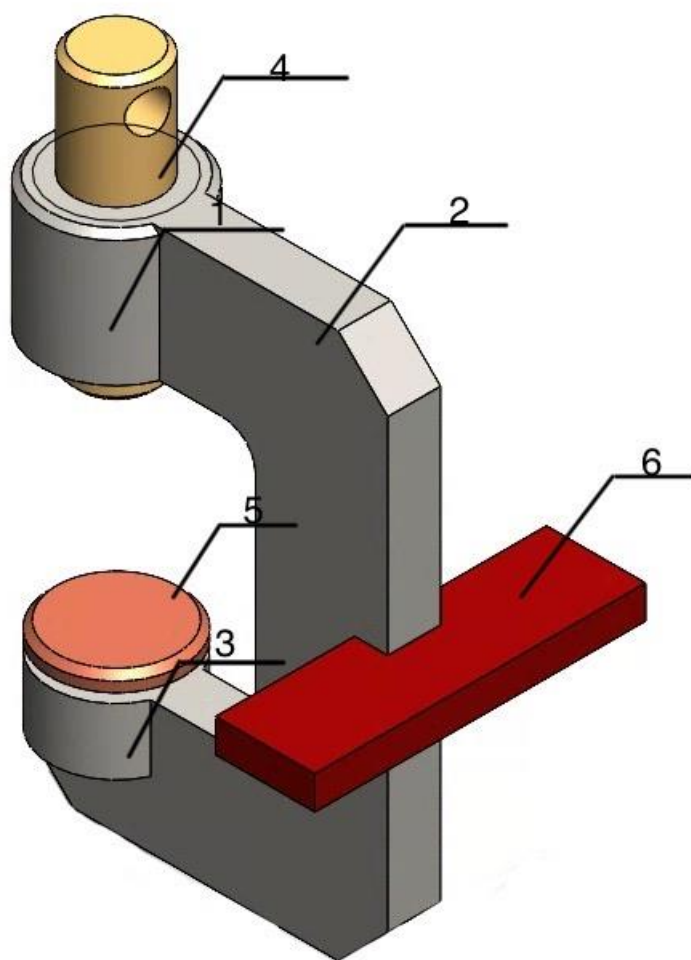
приспособления (струбцина) для выпрессовки и запрессовки подшипников карданных шарниров («Волга», «Газель», УАЗ, ЛуАЗ): 1 – гайка, 2 – скоба, 3 – втулка, 4 – винт, 5 – упор, 6 – планка
